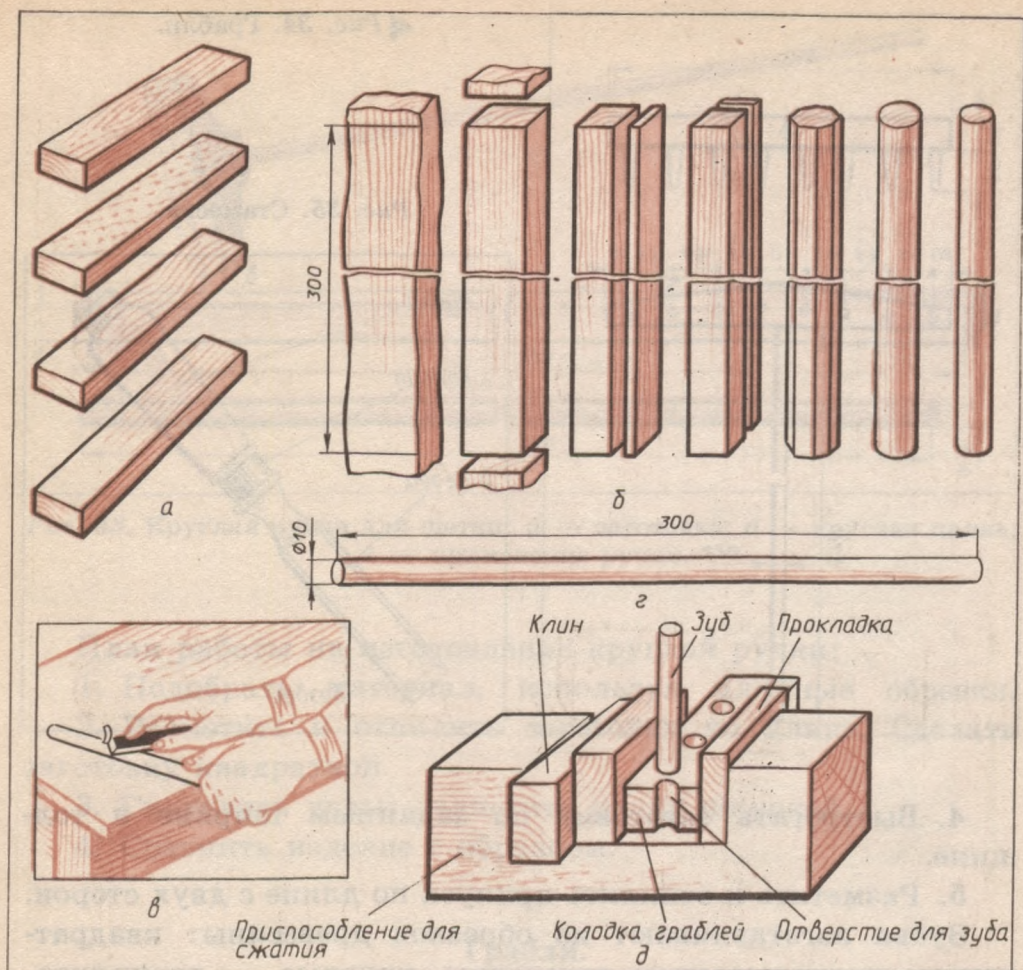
Изготовление и установка зубьев в колодку граблей: а — заготовки с различным расположением волокон; б — последовательность изготовления зубьев; в — обработка заготовки стамеской; г — заготовка для четырех зубьев; д — установка зубьев в колодку.
